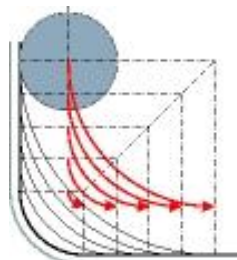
Dráhy nástroje při technologii iMachining [19]
